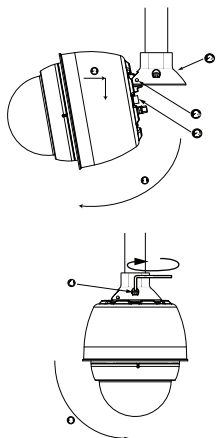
Fixation de la tête sur le support de montage parapet ou sur tube
